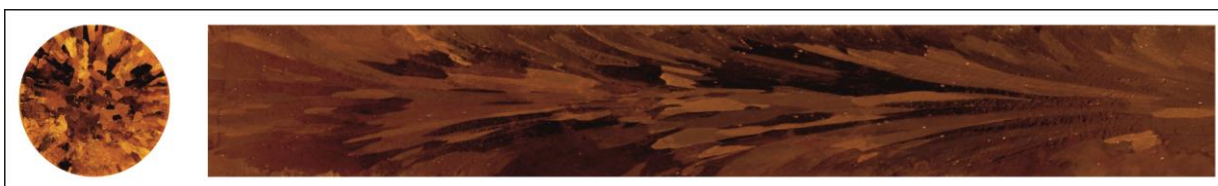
Makrostruktura przekroju poprzecznego i wzdłużnego pręta z miedzi w gatunku Cu-OFE uzyskanego w procesie ciągłego odlewania w warunkach laboratoryjnych na instalacji DCC-AGH przy prędkości odlewania 0,15 m/min. oraz przy przepływie wody chłodzącej na poziomie 0,4 l/min. w układzie pierwotnym i 0,8 l/min. w układzie wtórnym.
